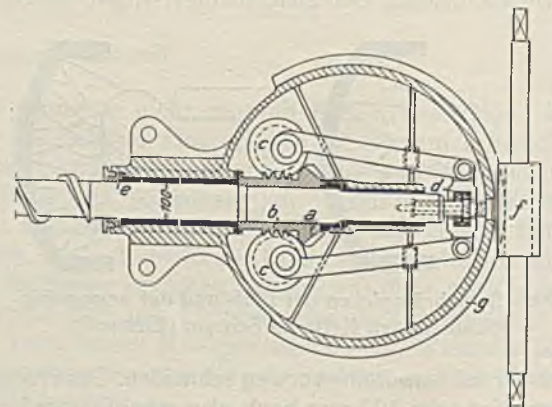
Getriebe für die Axialbewegung der Schrämstange (Eickhoff).
